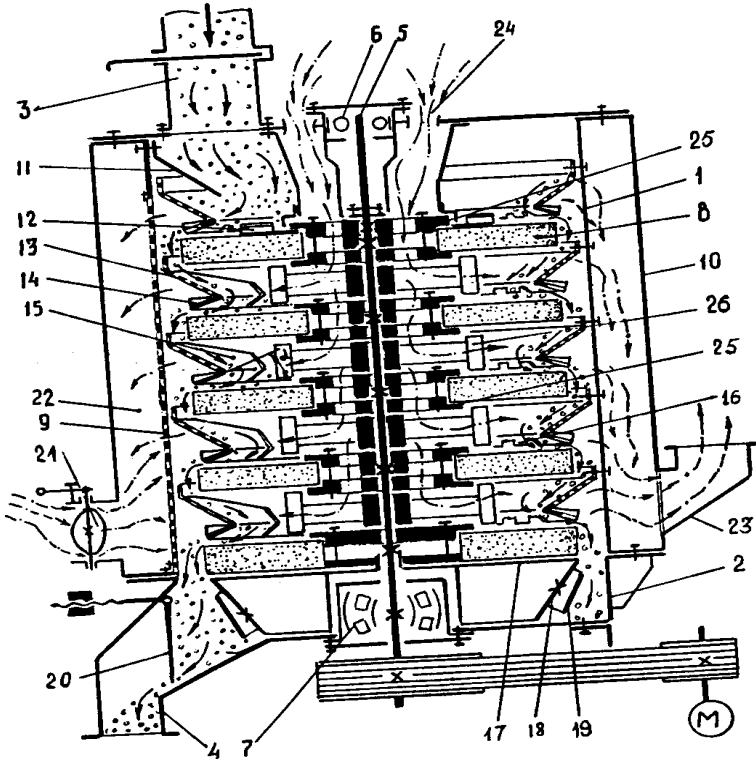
Принципова схема абразивно-дискової лущильно-шліфувальної машини
